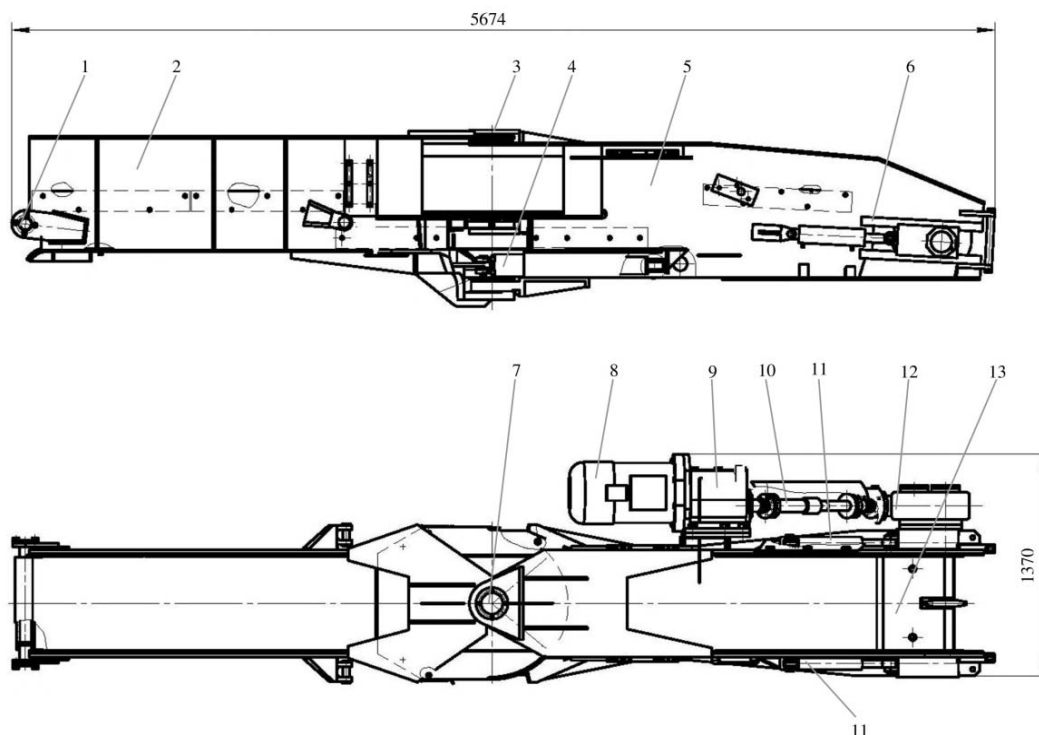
Конвейер-перегрузатель, скребковый. Общий вид
